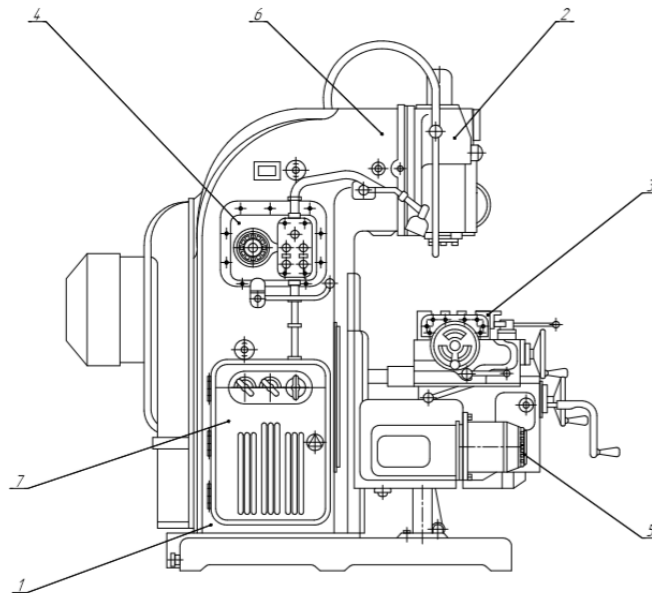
Загальний вигляд консольно-фрезерного верстату 6М12П.
